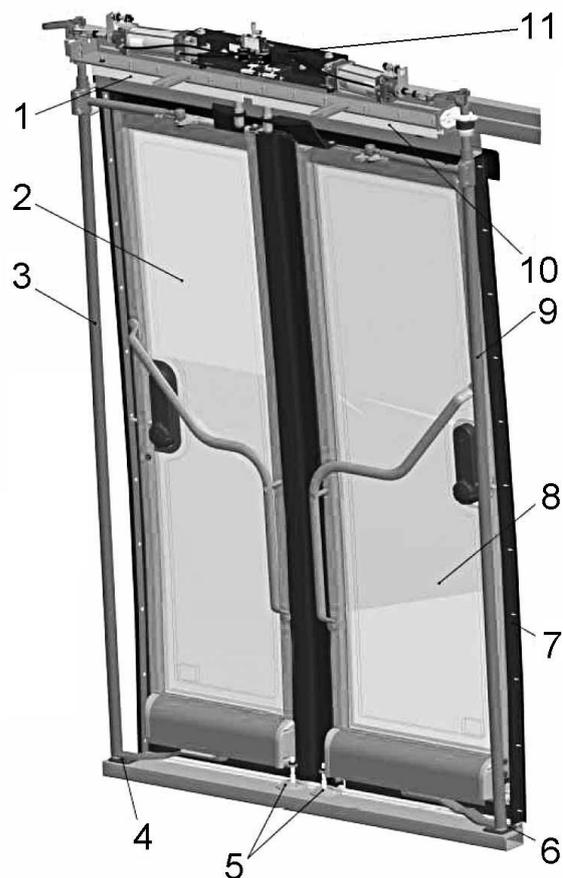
Дверь конструкции Camozzi:
